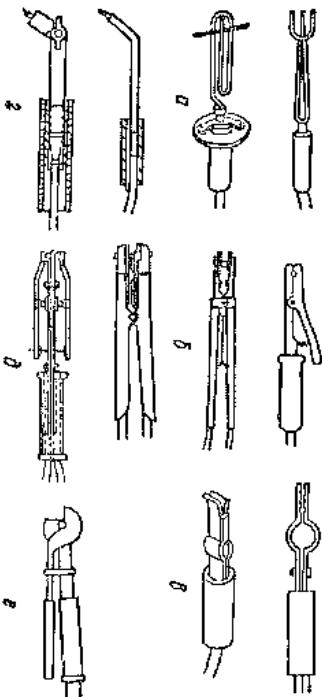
Конструктивные схемы электродержателей для ручной дуговой сварки:
